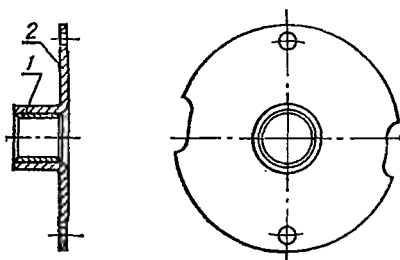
Держатель промежуточного подшипника стартера СТ8:
